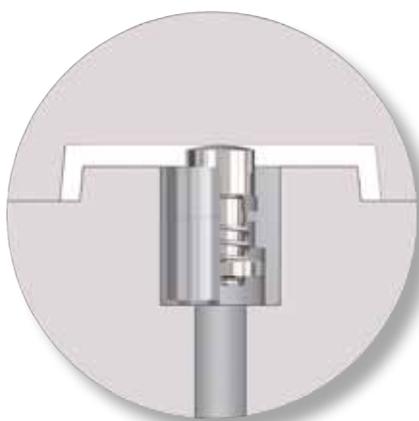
Sollte das Ventil klemmen oder die Druckluft noch anstehen (Steuerungsfehler), wird während der Schließbewegung des Spritzgießwerkzeuges der Kolben soweit zurückgedrückt, bis die Luftaustrittsbohrungen völlig verschlossen sind
